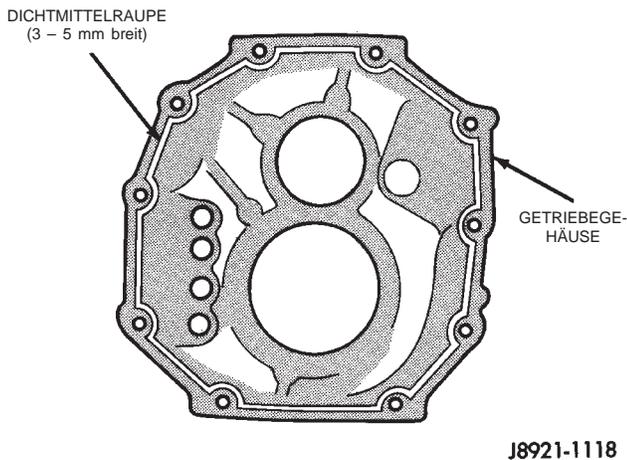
Dichtmittel auf Getriebegehäuse auftragen
